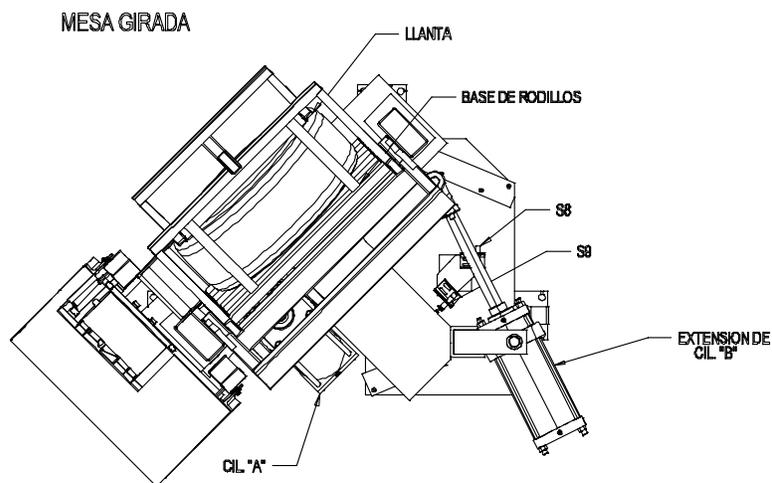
Vista en planta del giro de la herramienta.
